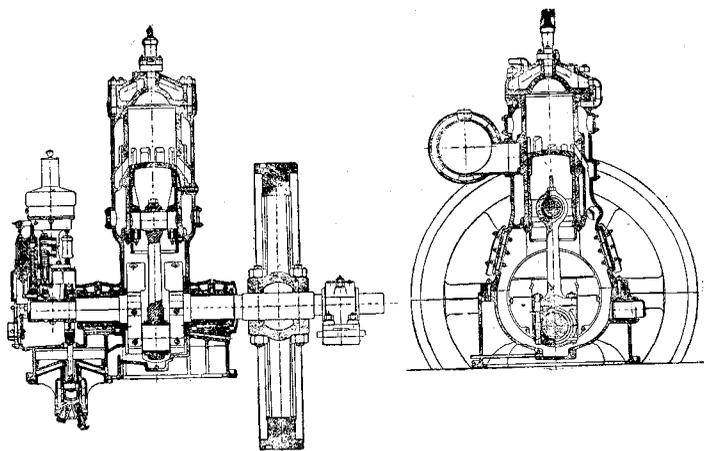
Продольный и поперечный разрезы бескомпрессорного двухтактного двигателя производства завода «Русский дизель»
